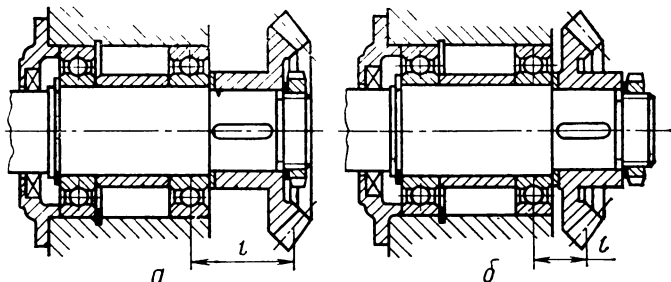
Конструктивные способы сокращения вылета консольной установки зубчатого колеса
